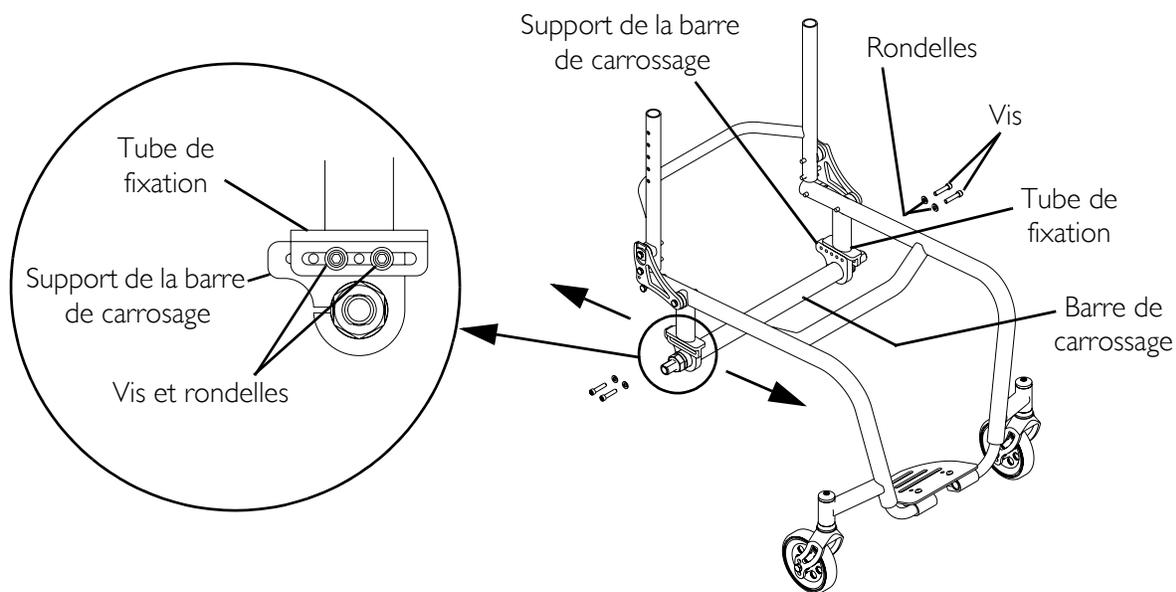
Déplacer les supports de la barre de carrossage
